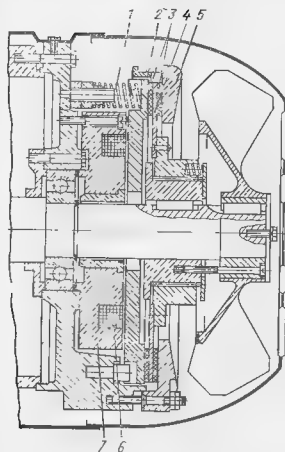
Тормозное устройство двигателя 4A160E.
